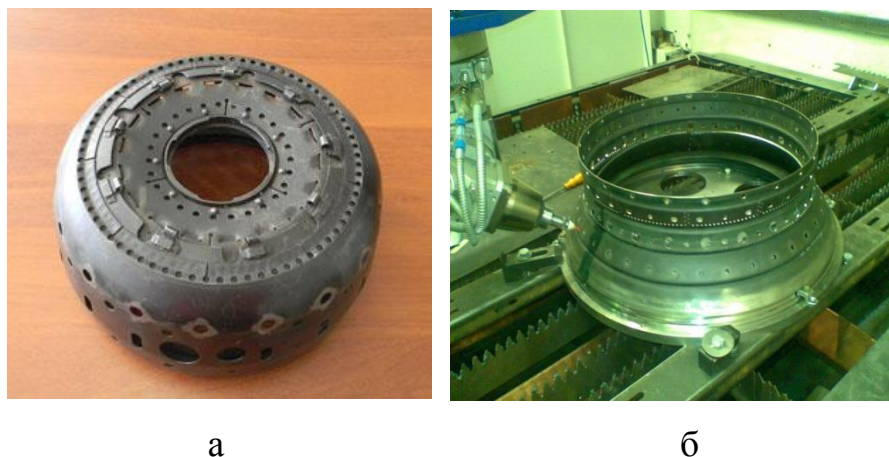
3D-лазерная вырезка отверстий в корпусе газогенератора двигателя – а;
